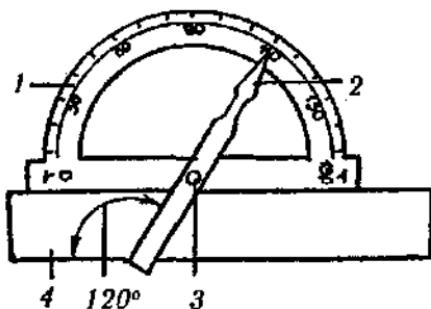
Угломер: 1 — шкала; 2 — стрелка; 3 — винт; 4 — деталь.
